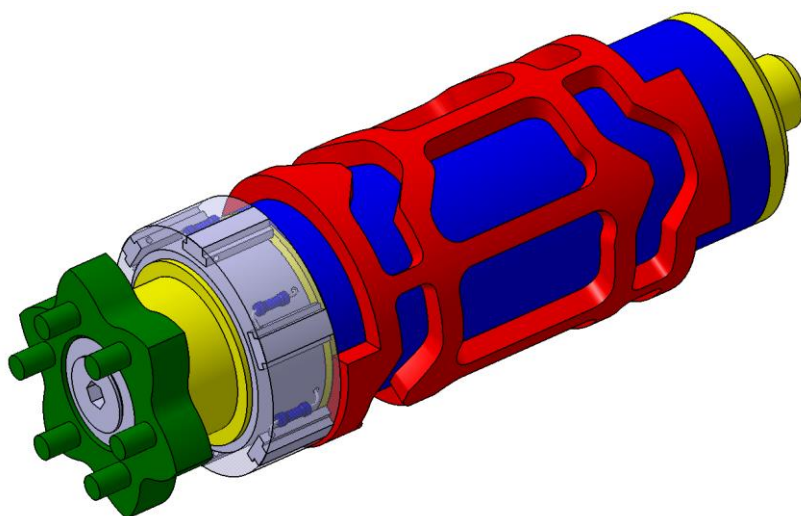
Polotovar bubínku s řadicími drahami řezanými laserem
